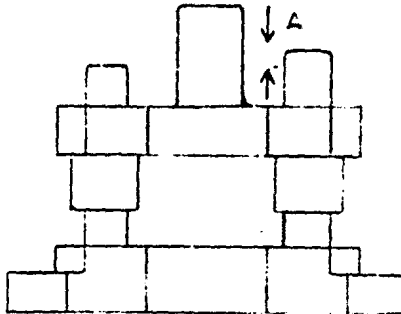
Columnas guía de distinta longitud para facilitar la colocación de la zapata sup.
